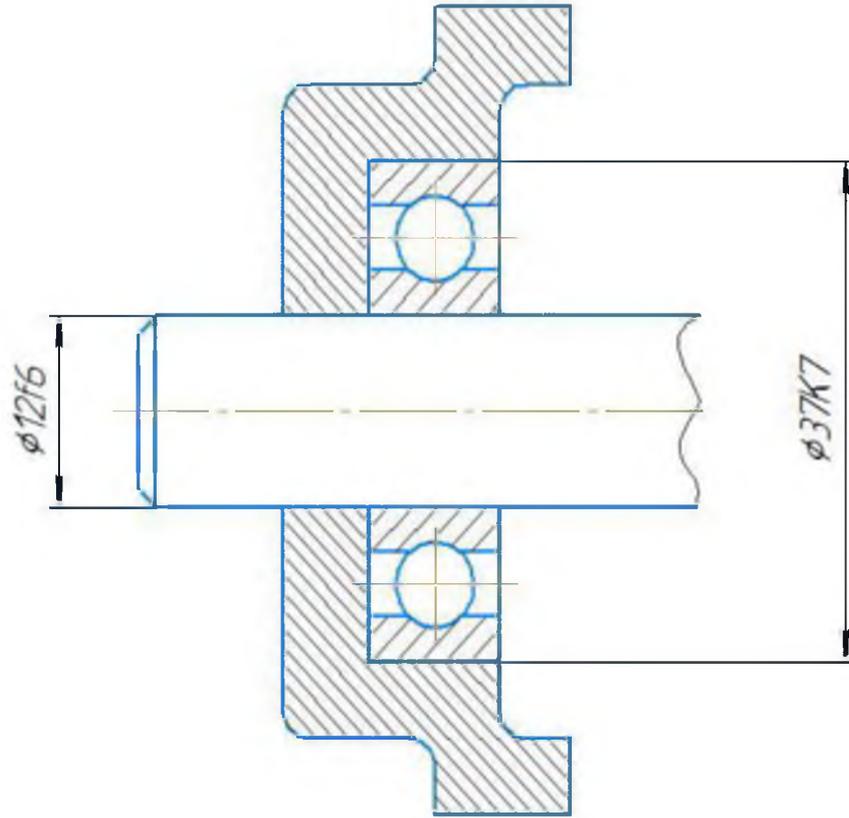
Узел выходного вала цилиндрического редуктора
